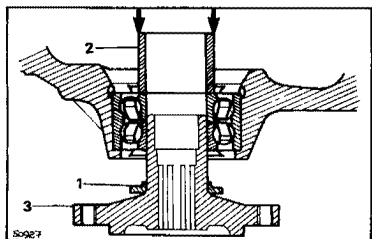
Насадка поворотного кулака на ступицу колеса
